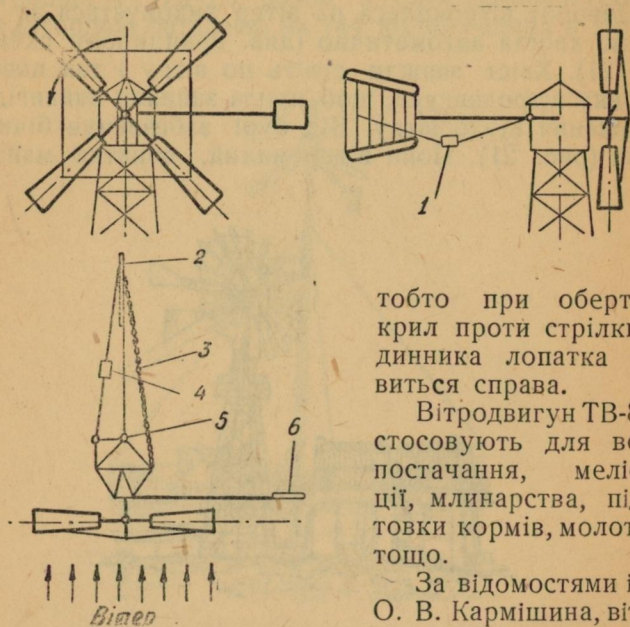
Схема пристрою для повертання крил: 1 — тягар; 2 — хвіст; 3 — ланцюг; 4 — трос; 5 — шарнір; 6 — бічна лопатка.
